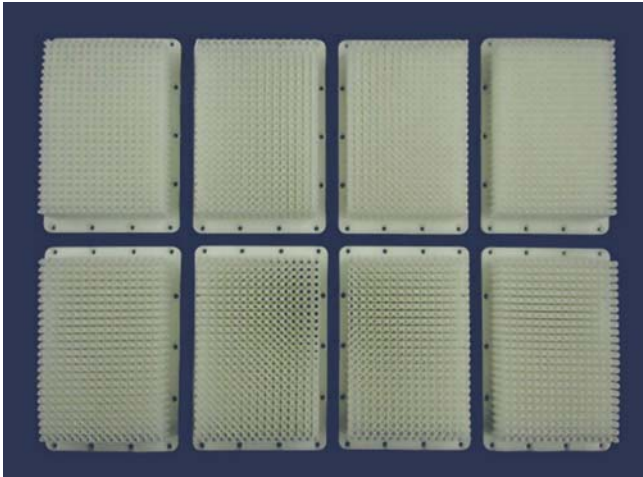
Definitive Geometrie der SLS-Teile (Bild irpd)
